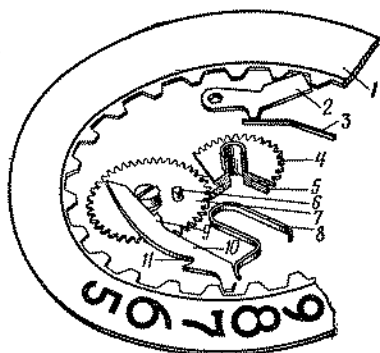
Кинематическая схема календарного устройства часов «Полет» 2616: 1 — диск календарный; 2 — фиксатор; 3 — пружина фиксирующего рычага; 4 — колесо часовое; 5 — колесо календаря первое; 6 — штифт; 7 — колесо календаря второе; 8 — пружина переключающего рычага; 9 — выступ упорный; 10 — рычаг переключающий; 11 — штифт
